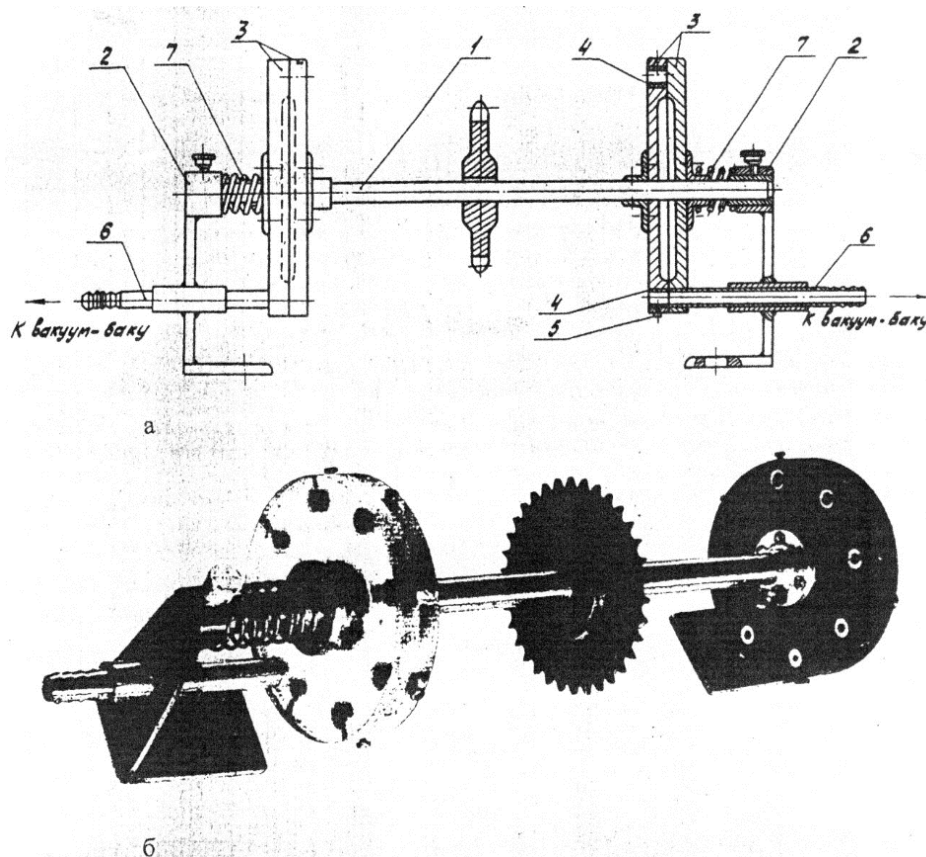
Роторное вакуумное устройство: а – схема, б – фотография
